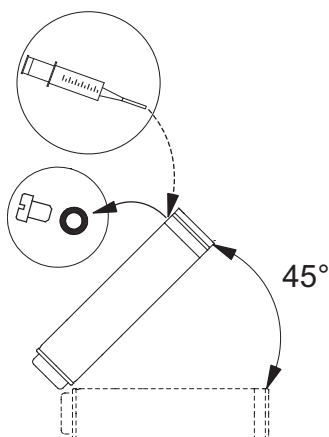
Posizione del motore durante il riempimento - MS 6000
